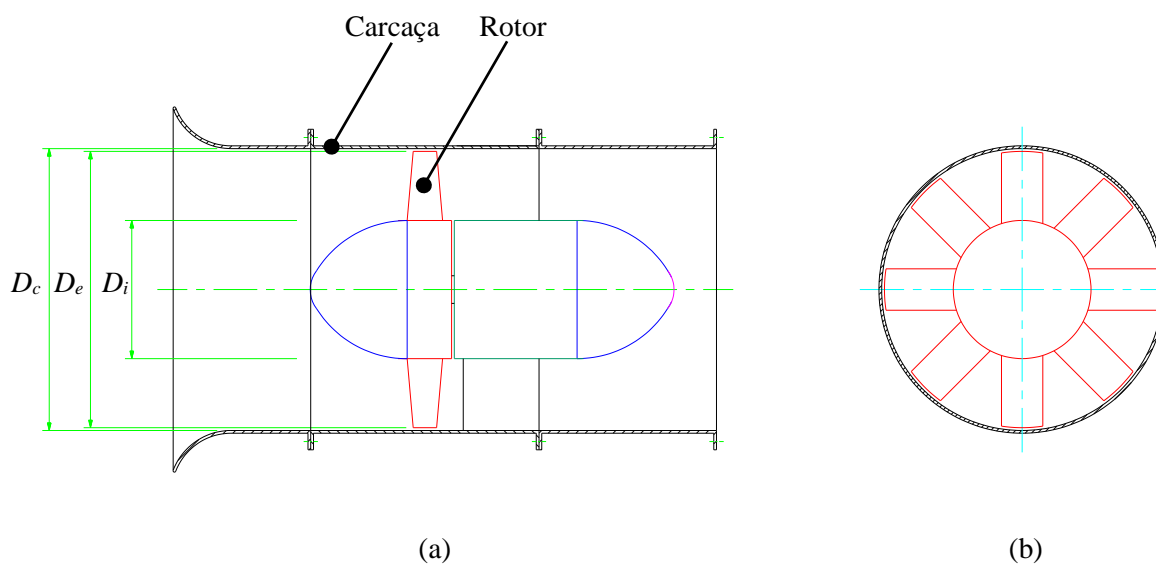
Esquema de um ventilador axial do tipo rotor e carcaça (tubeaxial): (a) seção longitudinal, (b) seção transversal do rotor
